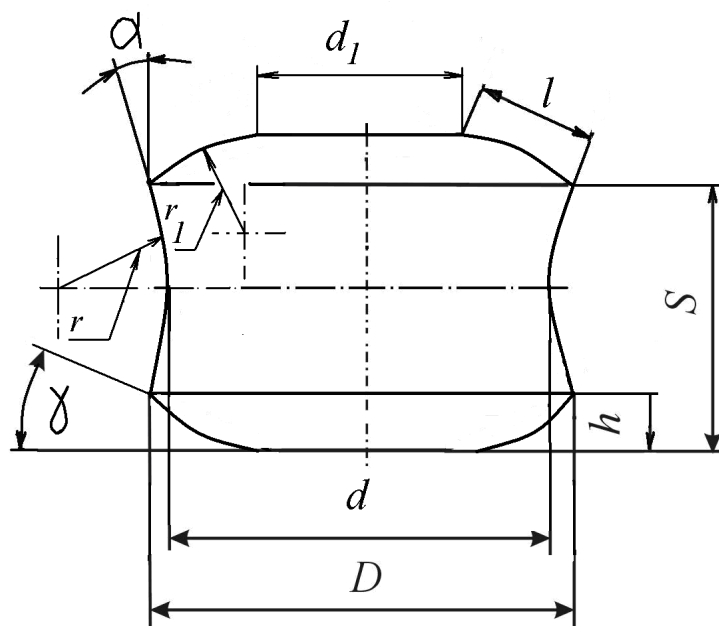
Режущая пластина из ПСТМ двусторонняя тороидная
